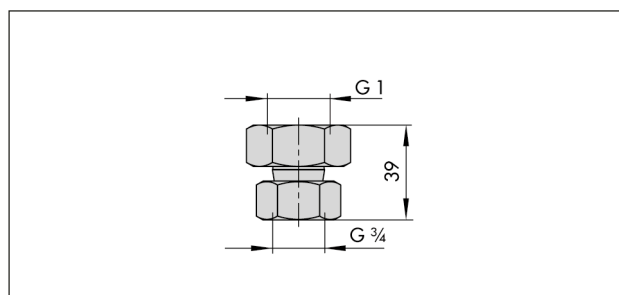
Anschlussstück für Ventil G1 (inkl. Dichtung)
